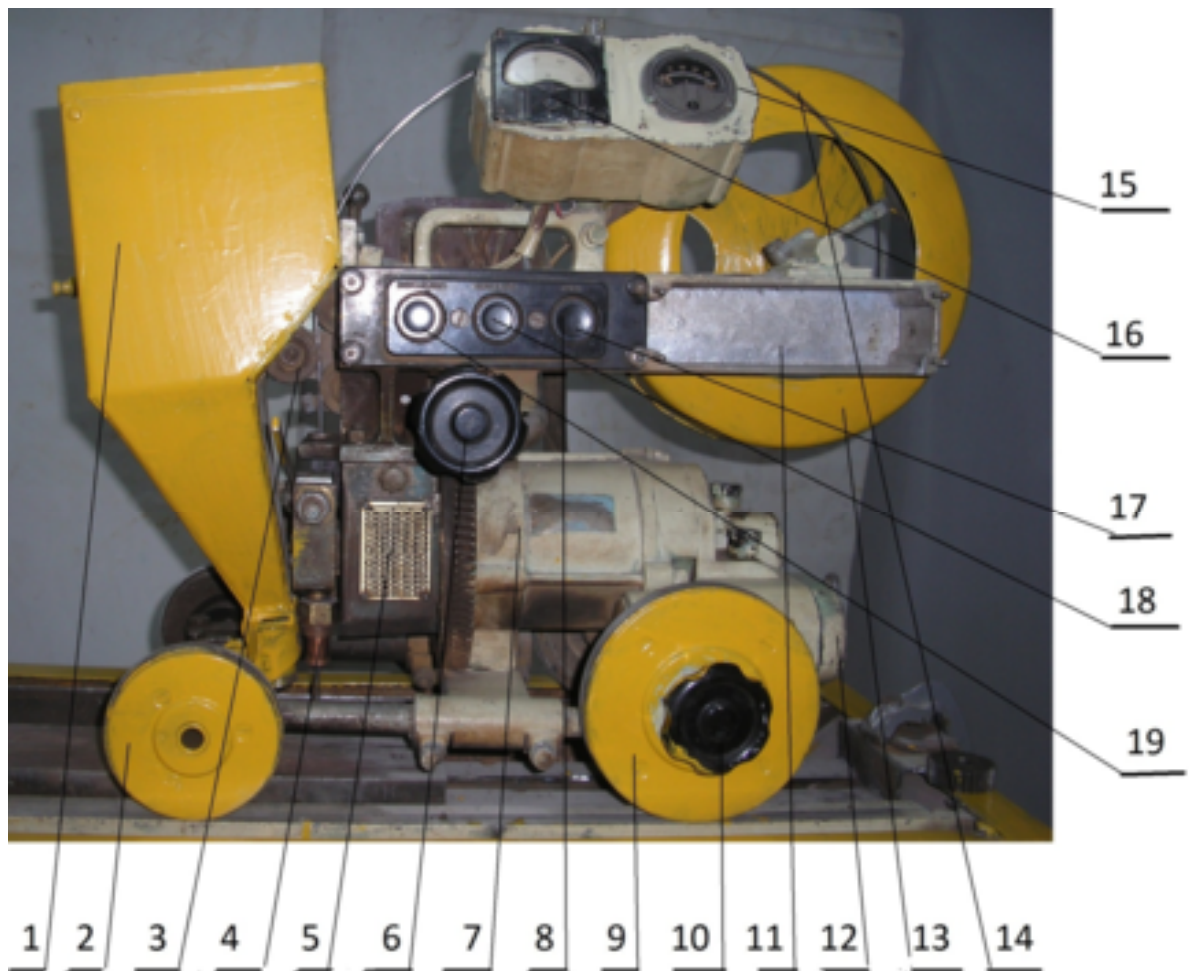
Устройство сварочного трактора ТС-17МУ:
